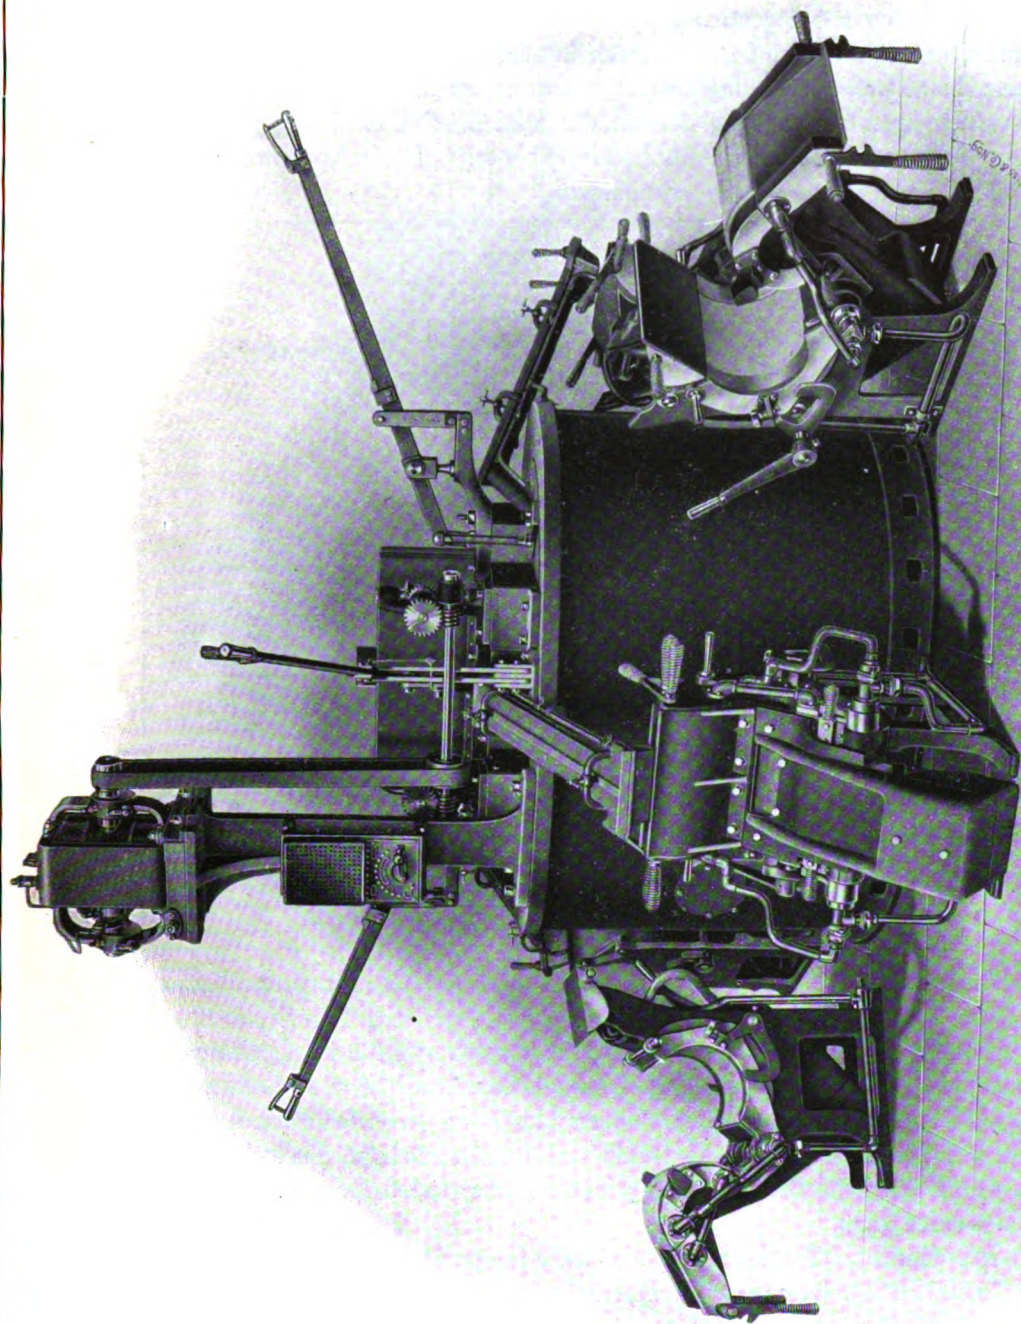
PLATTENGIESSWERK FÜR 2500 KG SCHMELZGUT MIT DREI METALLPUMPEN UND FÜNF PLATTENGIESSAPPARATEN MIT WASSER-
